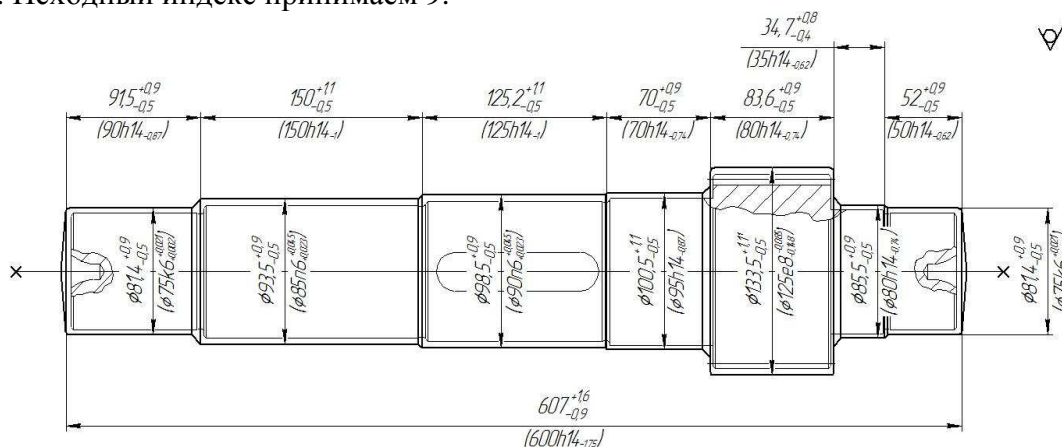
Эскизы цельно штампованной заготовки вала шлицевого
